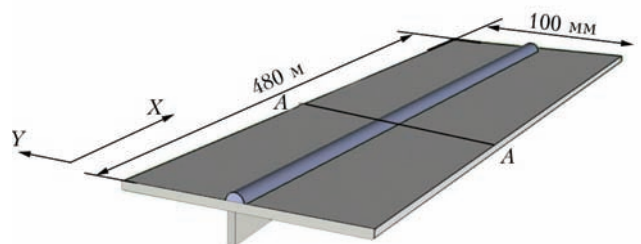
Схема сварного таврового соединения из титанового сплава ВТ-20
